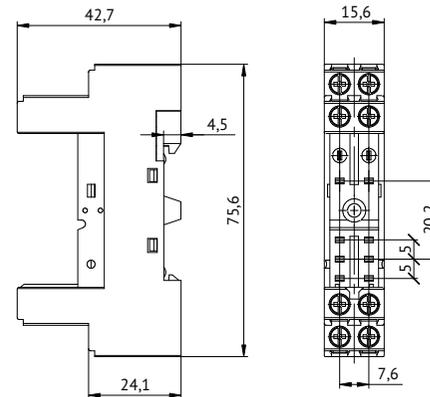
Габаритные, установочные и присоединительные размеры розетки OptiRel G RR95-82
